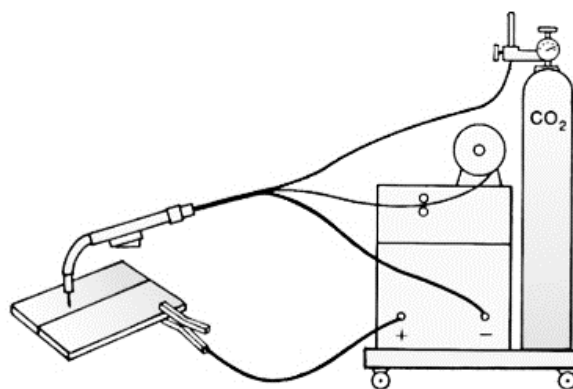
Máquina de soldadura MIG/MAG [20]
